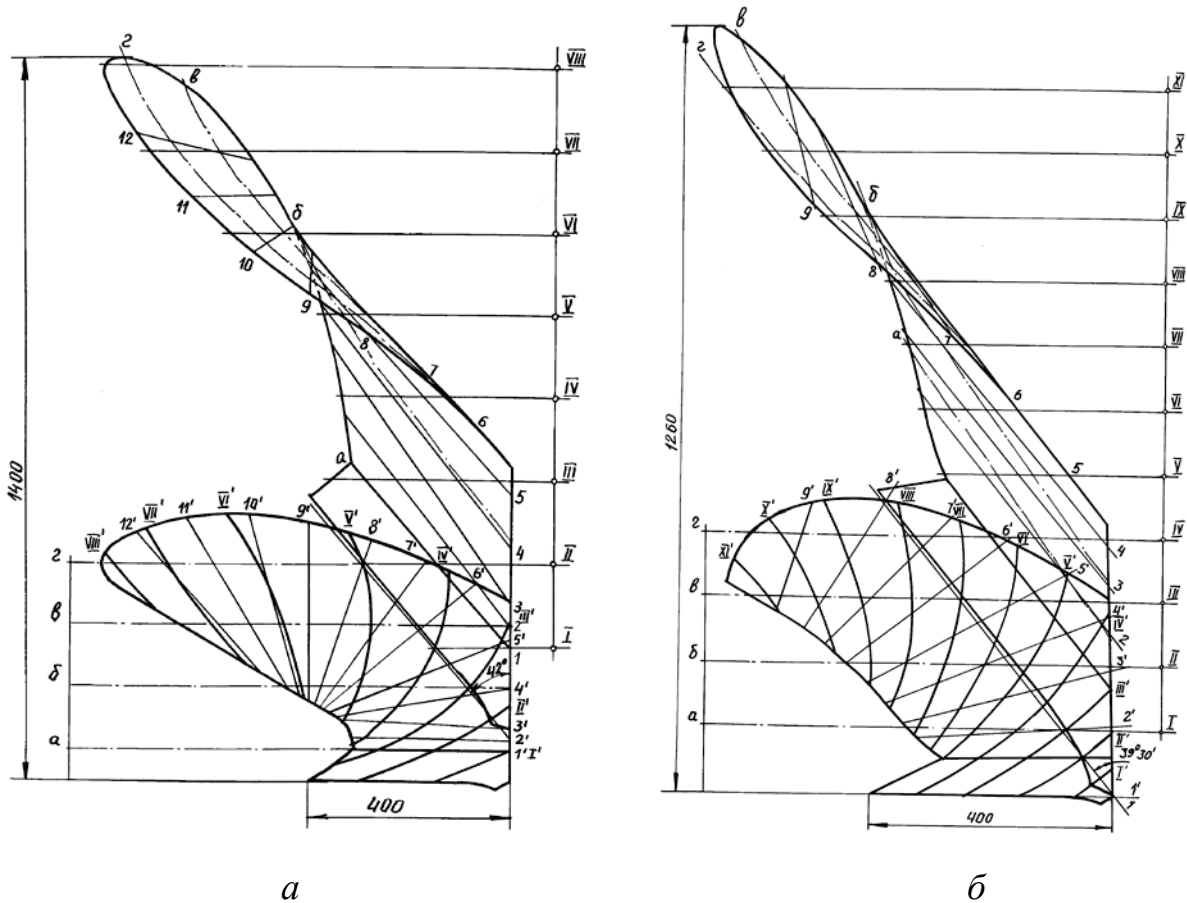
Схеми поверхонь плужних корпусів з торсовими поверхнями: *a* – КВУ.40.000; *б* – ККВ.01.000-01
